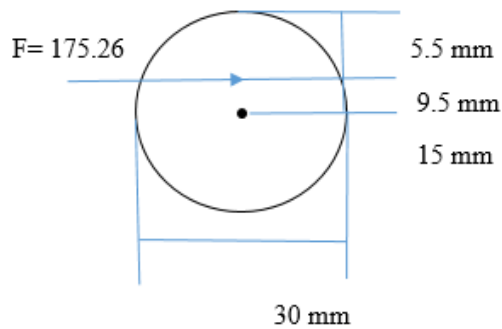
DLC de fuerzas en la polea principal de la maquina
